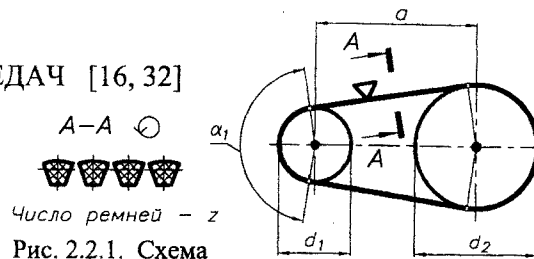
Схема и основные размеры клиноременной передачи
